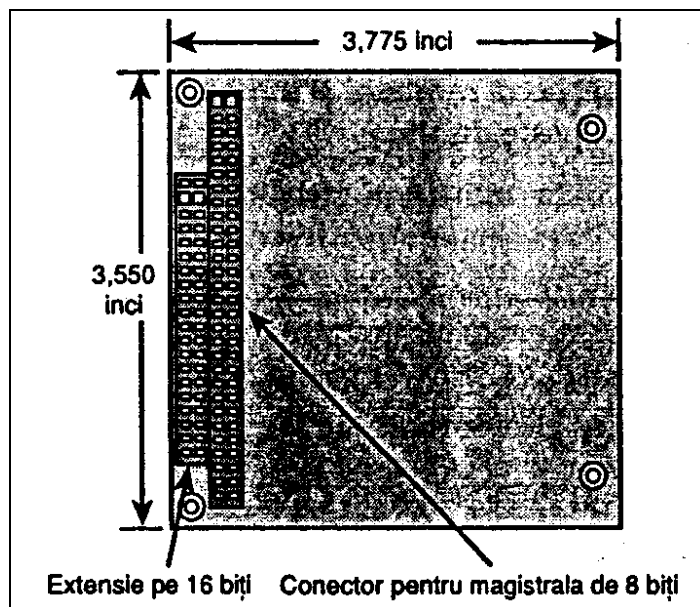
Dimensiunile plăcii de extensie PC/104
